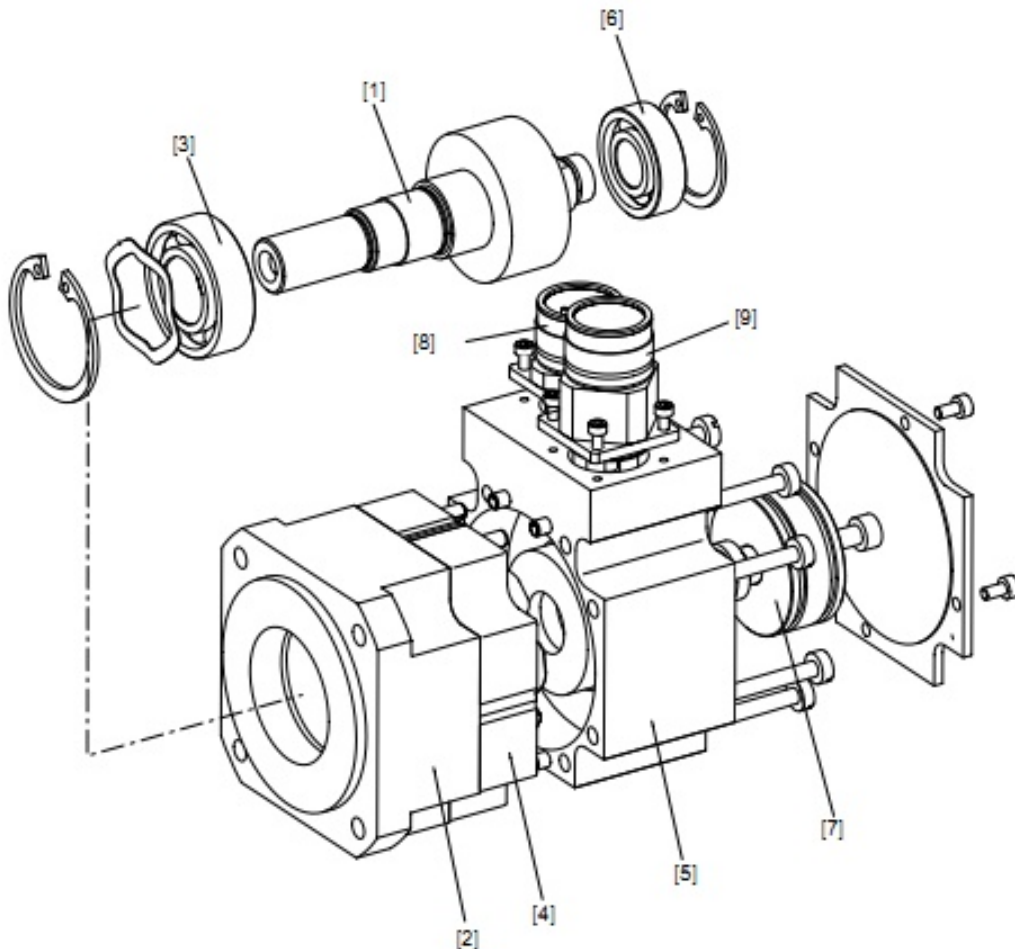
Будова синхронного серводвигуна CMD компанії SEW-EURODRIVE: 1 – ротор; 2 – підшипниковий щит з фланцем; 3 – радіальний шарикопідшипник; 4 – статор; 5 – задній підшипниковий щит; 6 – радіальний шарикопідшипник; 7 – резольвер; 8 – роз'єм сигнального кабелю; 9 – роз'єм силового кабелю
